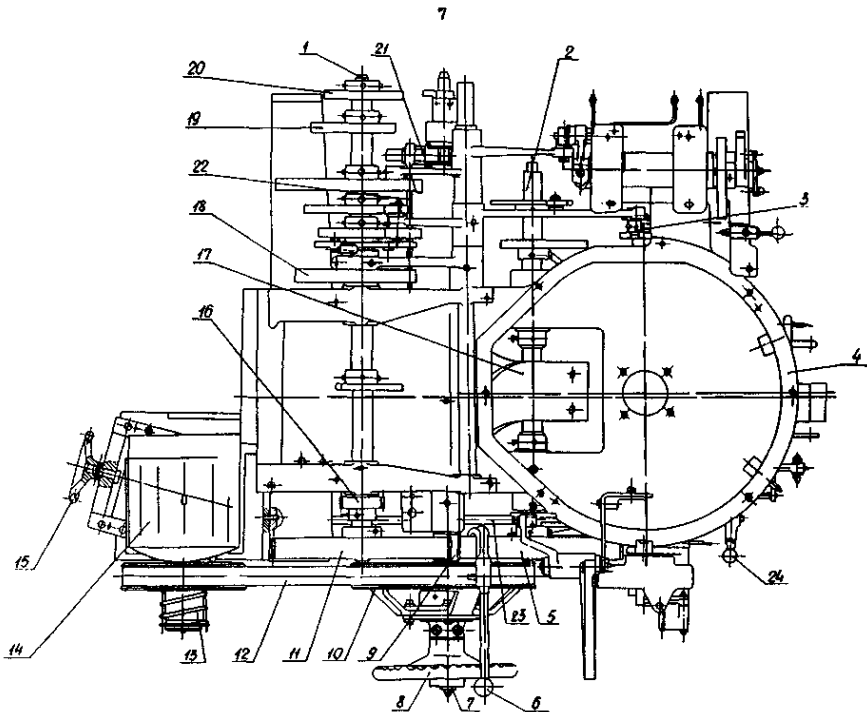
Станина з головним приводом автоматів АРТ і АР1С: 1, 2 - кулачкові вали; 3 - привід крана; 4 - станина (картер); 5, 11 - зубчасті колеса; 6, 24 - важелі; 7 - вал зчеплення; 8, 15 - маховики; 9, 16 - шестірни; 10 - шків; 12 - клиноподібний пас; 13 - варіатор; 14 - електродвигун; 17, 18, 19, 20 - кулачки; 21 - зчеплення; 22 - тяга; 23 - вал
